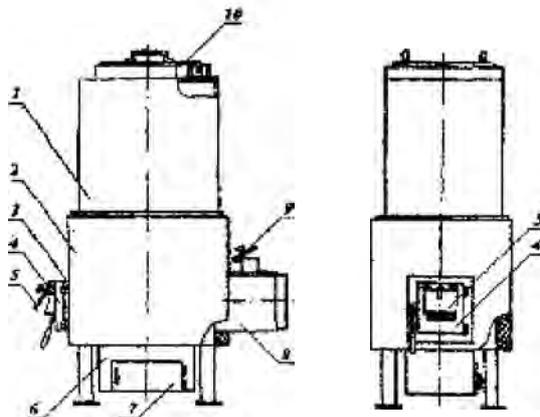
Схема газогенератора [2]: 1 – топливный бункер; 2 – камера газификации; 3 – горловина; 4 – дверца горловины; 5 – заслонка первичного воздуха; 6 – зольник; 7 – дверца зольника; 8 – жаровая труба; 9 – заслонка вторичного воздуха; 10 – крышка бункера
